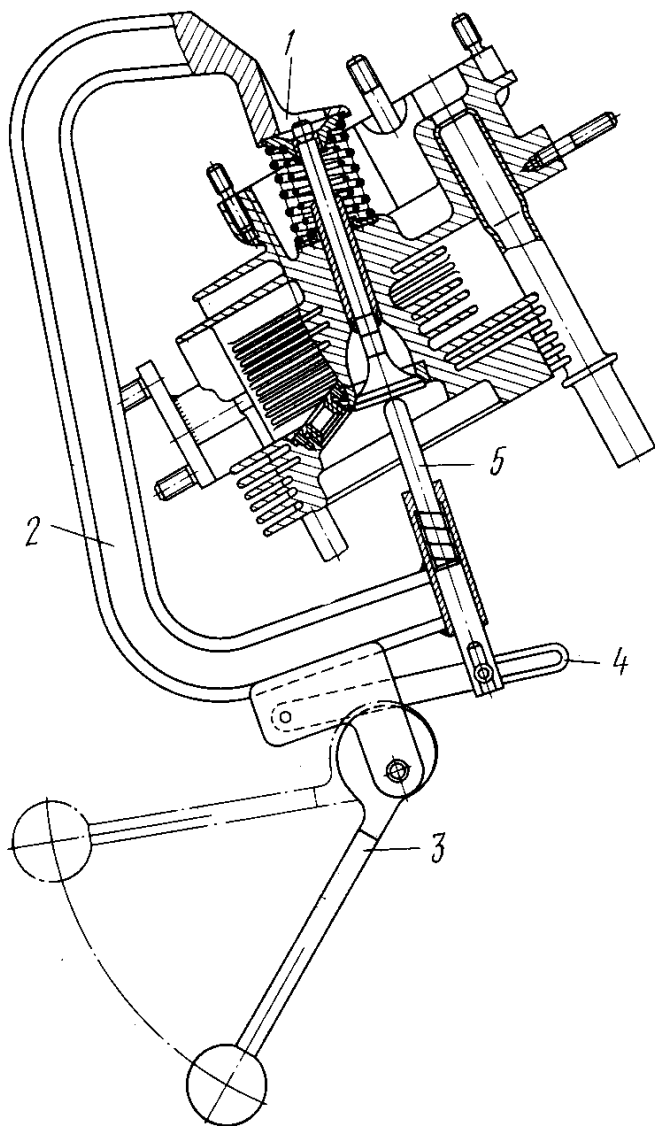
Съемник пружин клапана: 1—кольцевой упор; 2—скобка; 3—рычаг с кулачком; 4—планка; 5—шток
